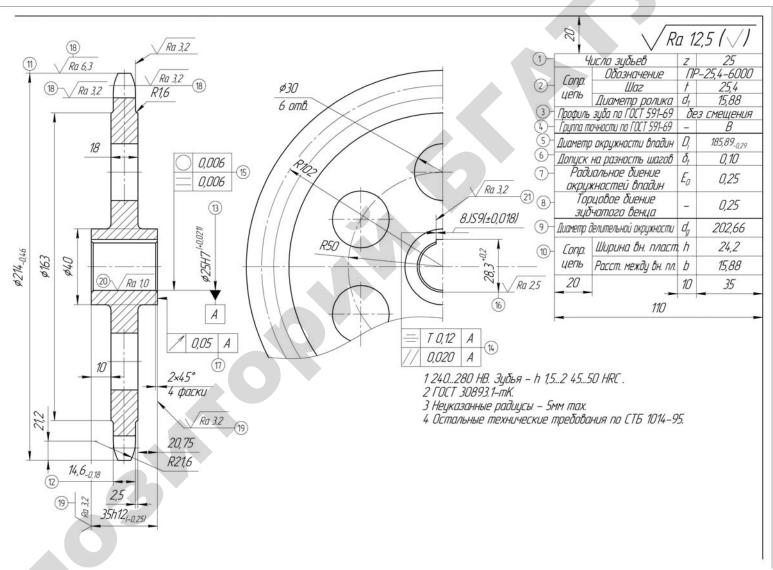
Схема простановки размеров и показателей точности для звездочки
